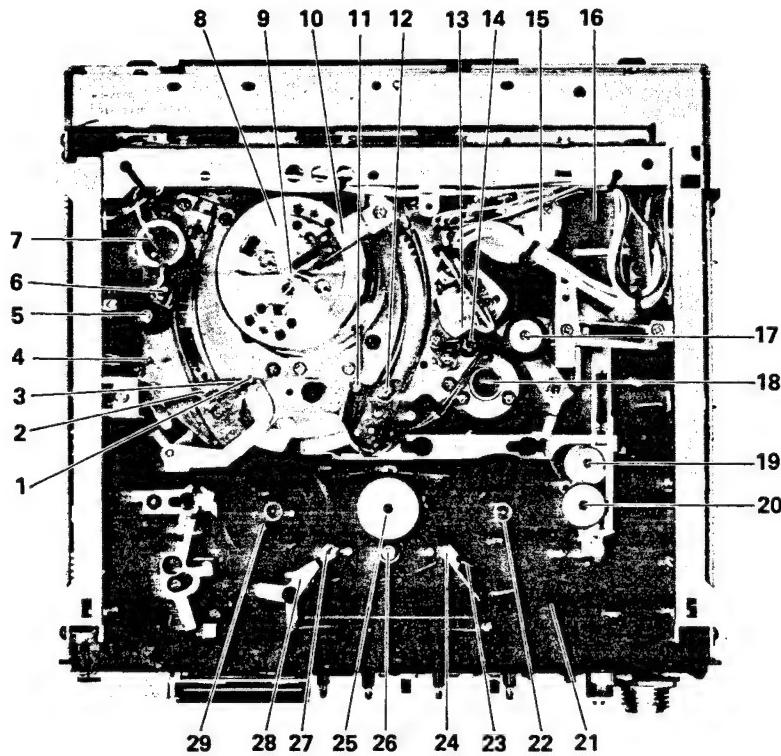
Fig. 1-4 Draufsicht Top view
